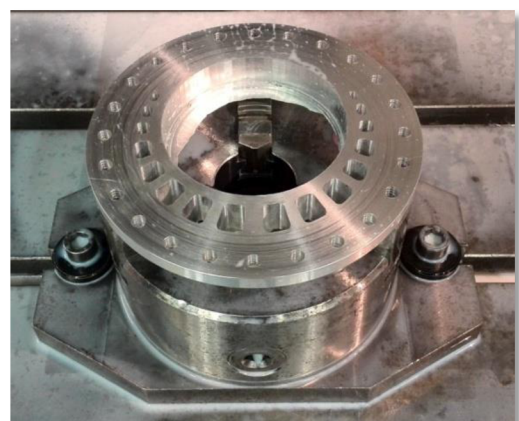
Tvar součásti po obrobení frézou o Ø 4 mm.
